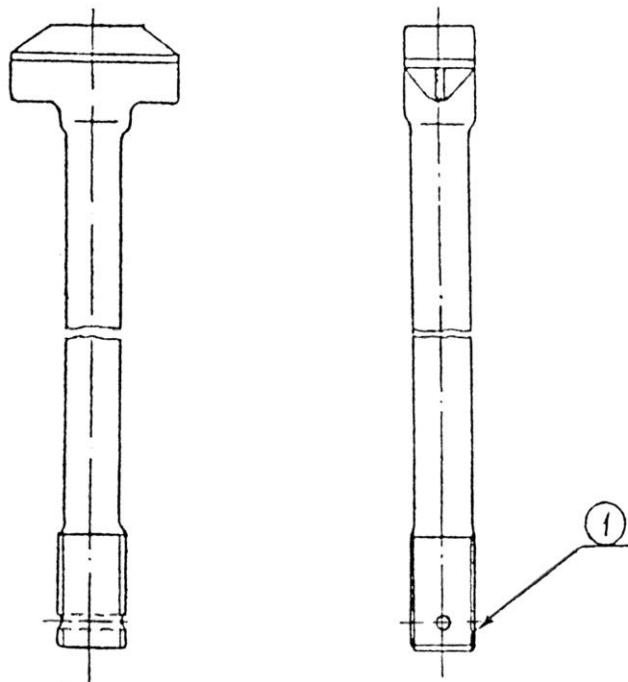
Поверхность износа предохранительного стержня тележки КВЗ-ЦНИИ тип I
